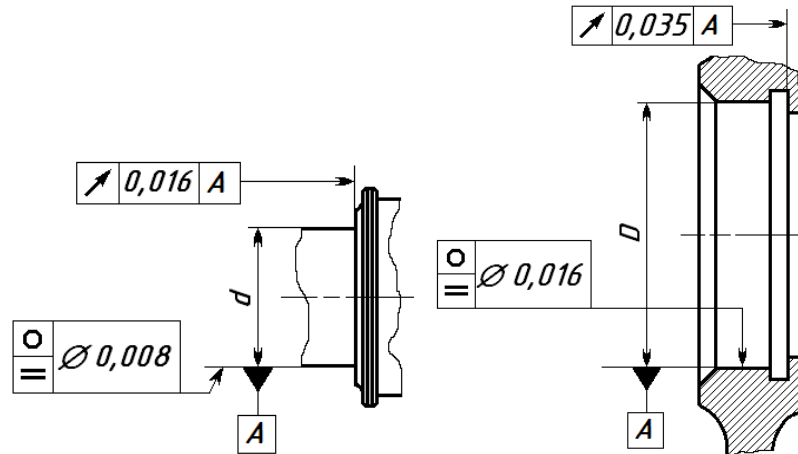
Нанесение на чертеже требований к параметрам формы и расположения посадочных поверхностей под подшипник
